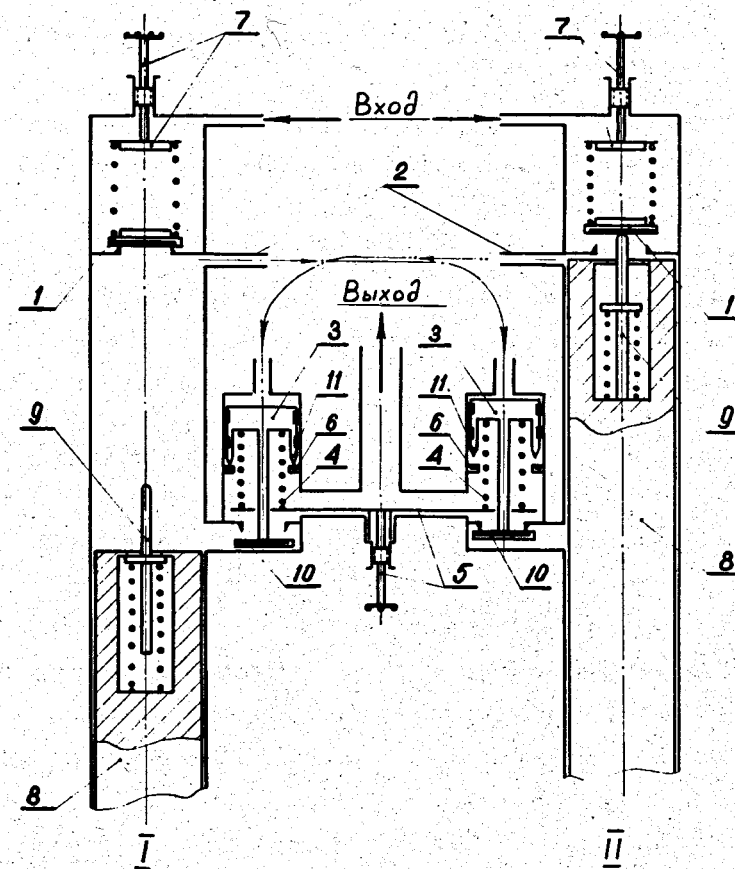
Схема детандера: 1 - клапаны впуска; 2 - газовые каналы; 3 - поршни сервоприводов; 4 - пружины; 5 - механизм регулировки отсечки выпуска; 6 - ограничители хода сервопривода; 7 - регуляторы отсечки впуска; 8 - поршни; 9 - механизм приводов впускных клапанов; 10 - клапаны выпуска, 11 - кромка поршня сервопривода.
